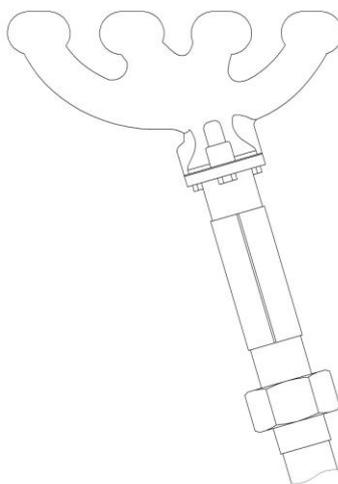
Крепление металлорукова к выпускному коллектору.
